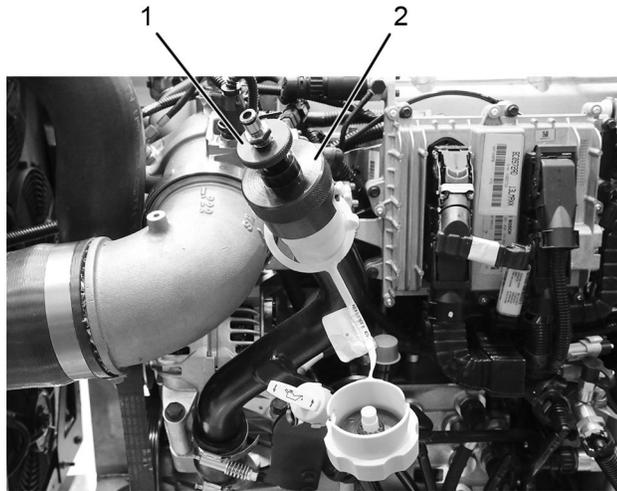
12-999-05-11 Plaque d'obturation du compresseur d'air
